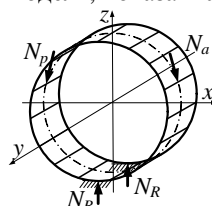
Схема нагружения полимерного сепаратора усовершенствованной конструкции
